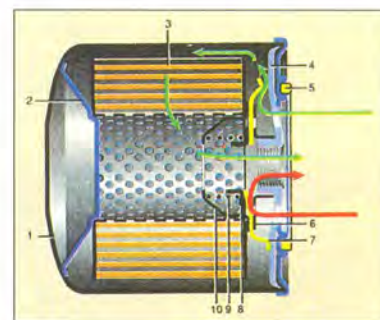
Масляный фильтр "Пюролатор" (Purolator) L10101: Габаритные размеры: диаметр – 93,5, высота – 67 мм. 1 – корпус; 2 – тарельчатая пружина; 3 – фильтрующий элемент; 4 – основание; 5 – резиновая прокладка; 6 – втулка, приваренная к корпусу блока клапанов; 7 – резиновая манжета перепускного и противодренажного клапанов; 8 – тарелка перепускного клапана; 9 – пружина приваренная к корпусу блока клапанов; 10 – корпус блока клапанов.
